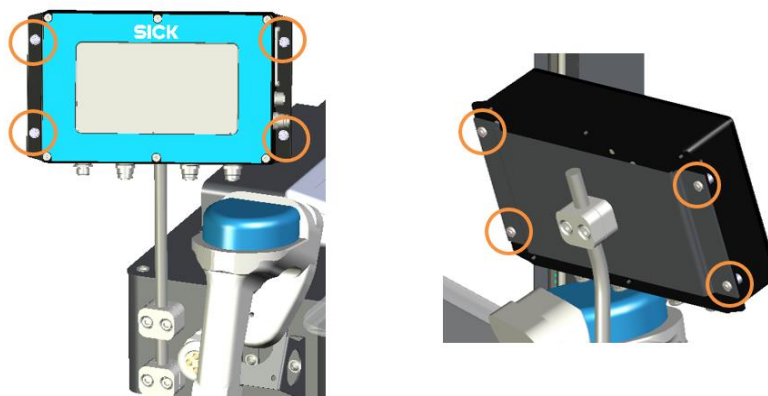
Cambio de componentes - pantalla (desmontaje/montaje)
